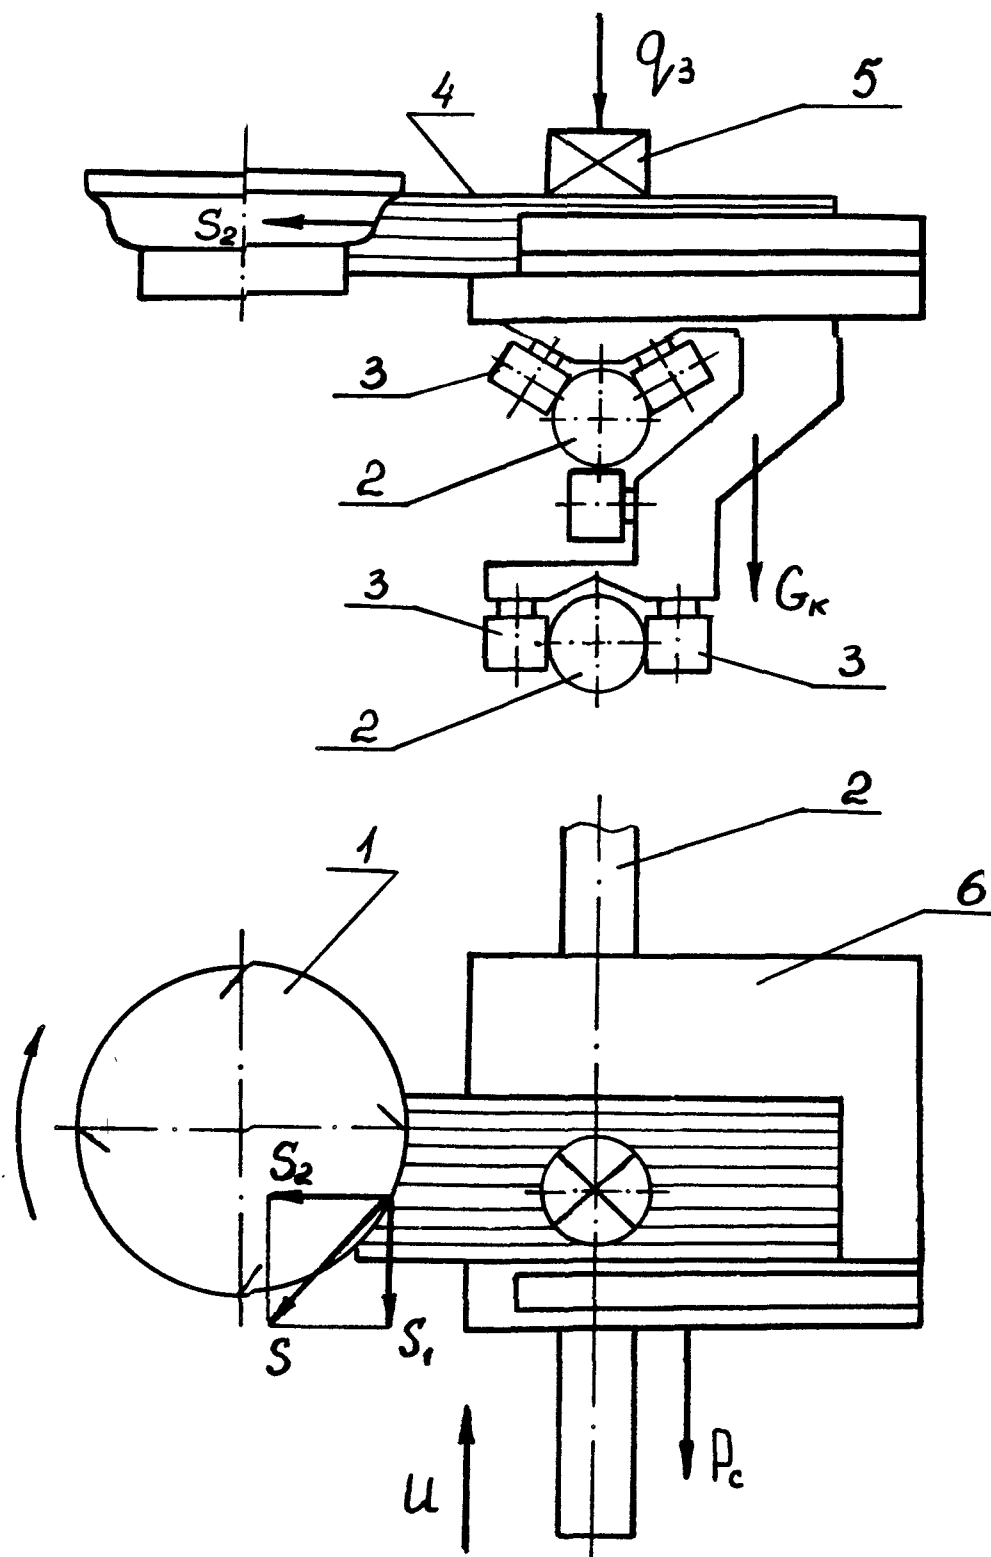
Функциональная схема фрезерного станка с шипорезной кареткой: 1 - фреза; 2 - направляющая; 3 - опора качения; 4 - заготовка; 5 - зажим; 6 - каретка
